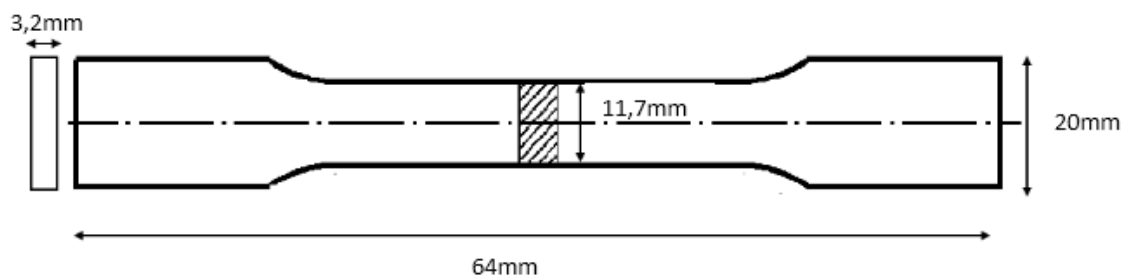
Ilustração do corpo de prova obtido por moldagem por injeção.
